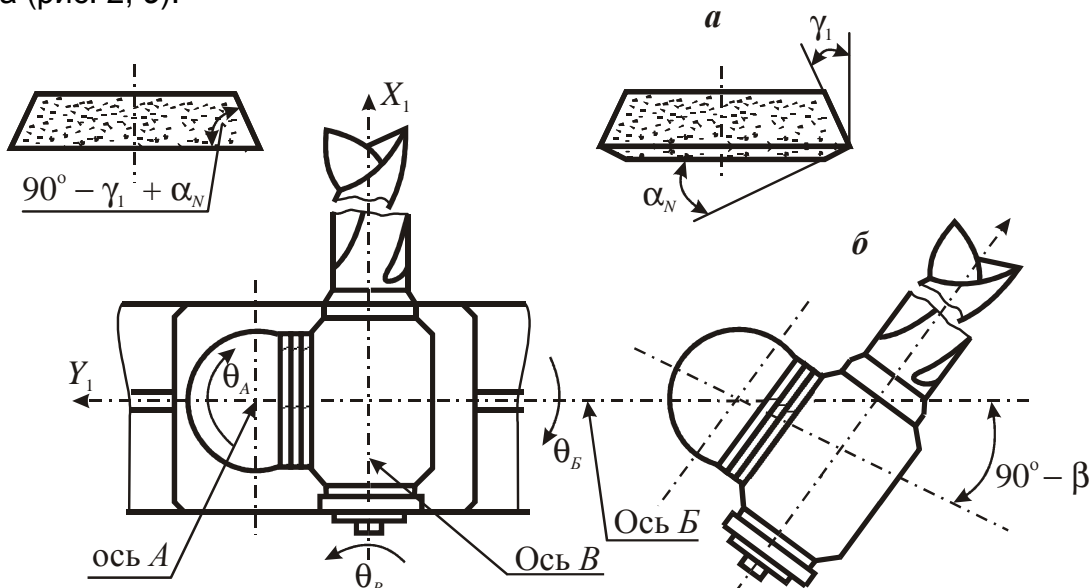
Схема установки сверла с ПРК в универсально-заточной головке
